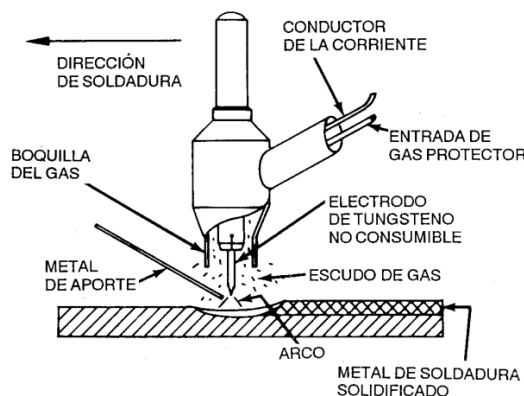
Proceso de soldadura GTAW [31]
